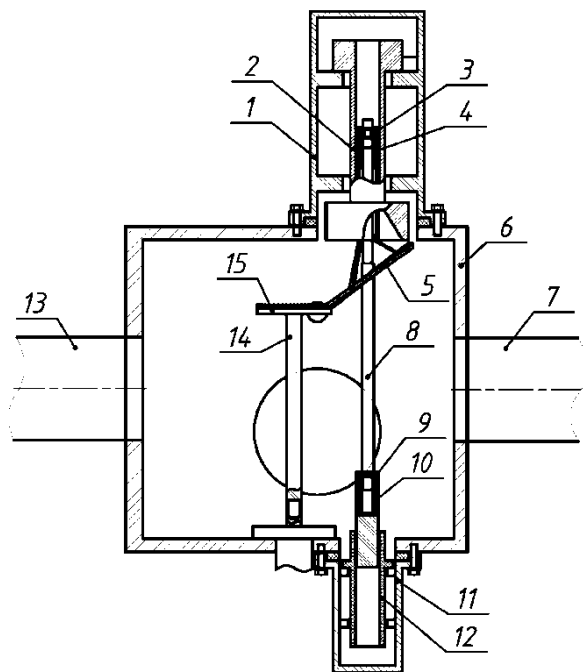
Предлагаемая схема модернизации камеры установки ННВ-6.6-И1 с вертикальным расположением упрочняемого изделия (вид спереди): 1, 11 — цилиндры; 2, 12 — направляющие; 3, 10 — крепления; 4, 9 — зажимы; 5 — кольцо; 6 — корпус вакуумной камеры; 7, 13 — катодные узлы; 8 — протяжка; 14 — вал; 15 — диск
